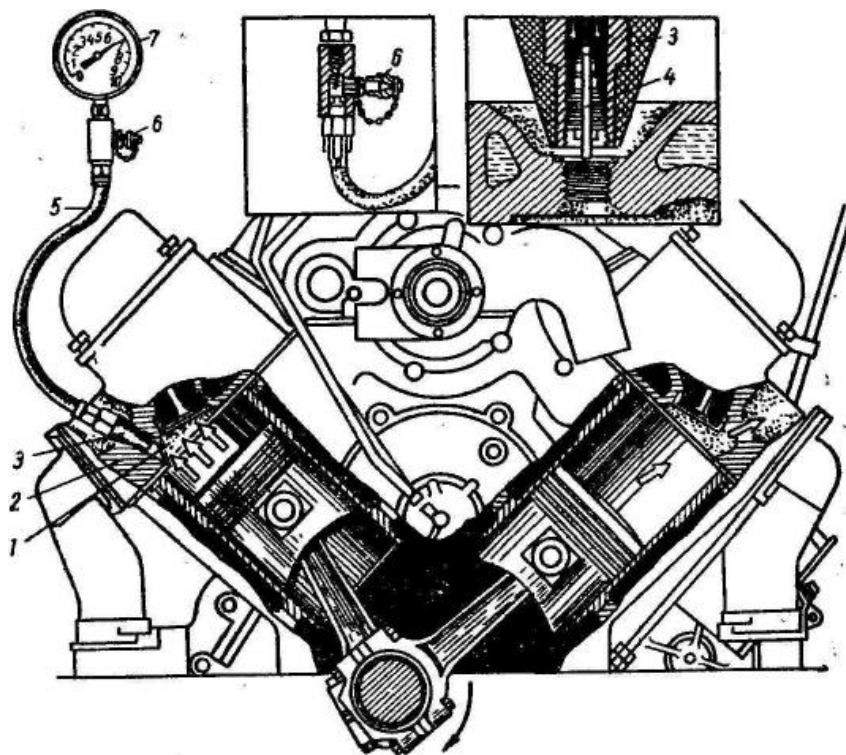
Схема установки для перевірки величини компресії в циліндрах двигуна автомобіля:
